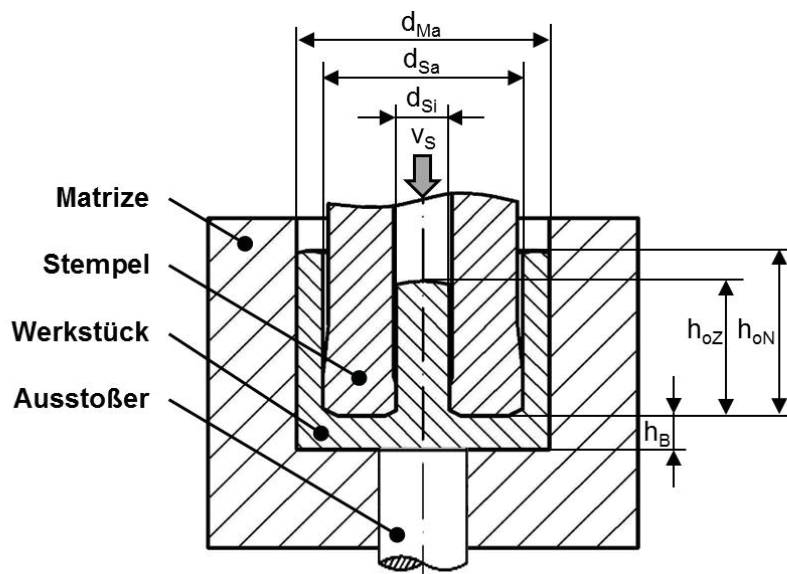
Prinzipskizze des VR-NR-FP mit einem bewegten Werkzeugelement (Stempel)
